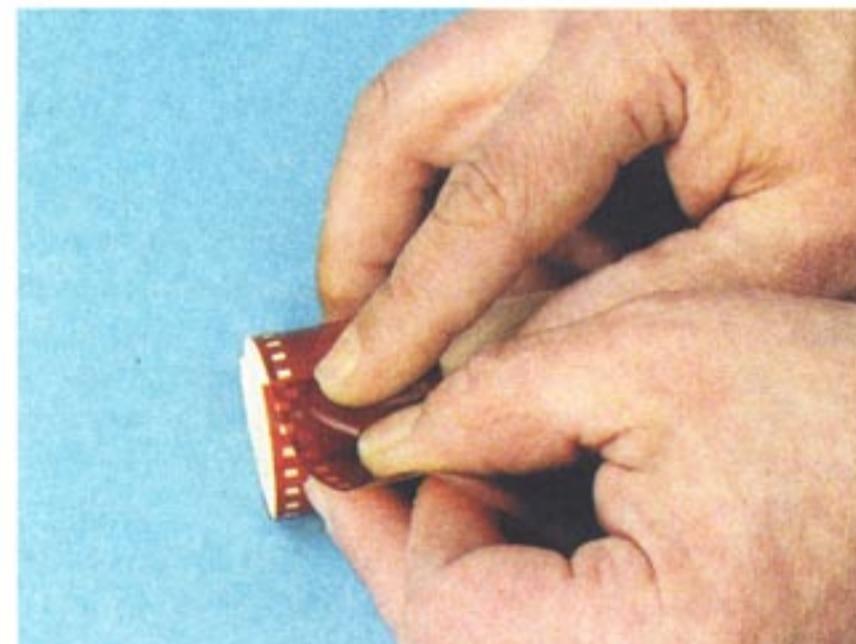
Измерение окружности заготовки с помощью фотопленки
